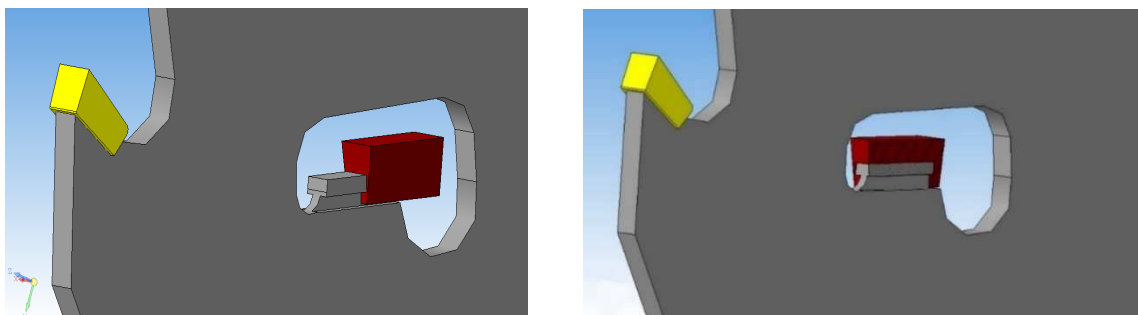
Схема крепления стабилизирующего ножа к полотну пилы
